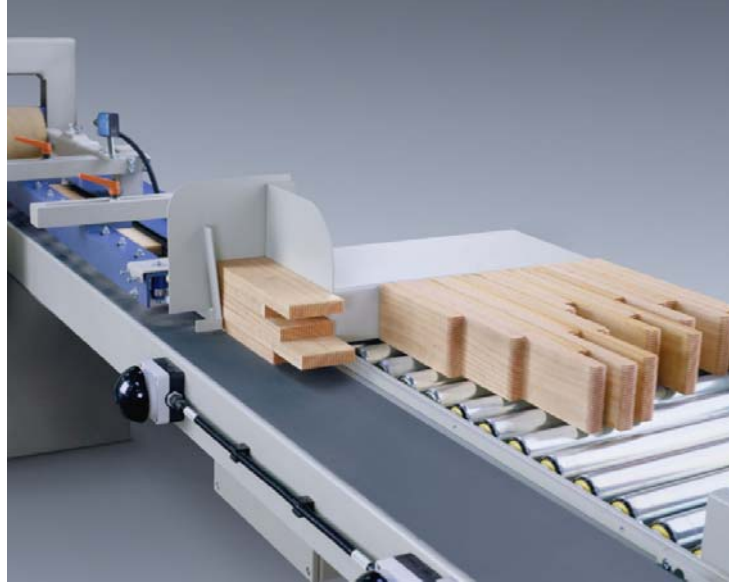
Finger joint makinesinde parmak dişlerin açılması (Grecon,2010)
